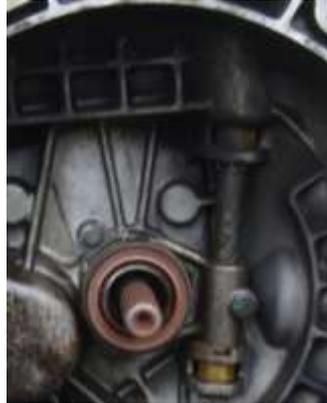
Desmontaje de Rodamiento, Horquilla, Palanca y Canastas de Embrague
